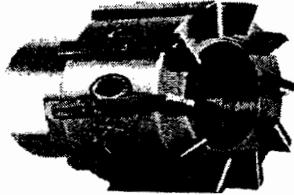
Side-Milling Cutter เป็นดอกกัดที่มีคมตัดด้านข้างทั้งสองข้าง
